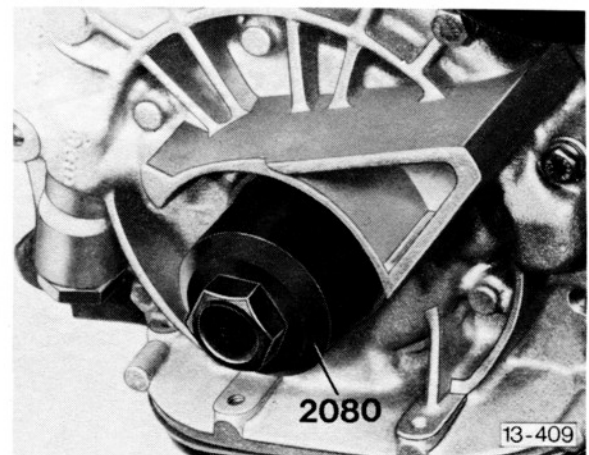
Dichtring Kurbelwelle Riemenscheiben-
